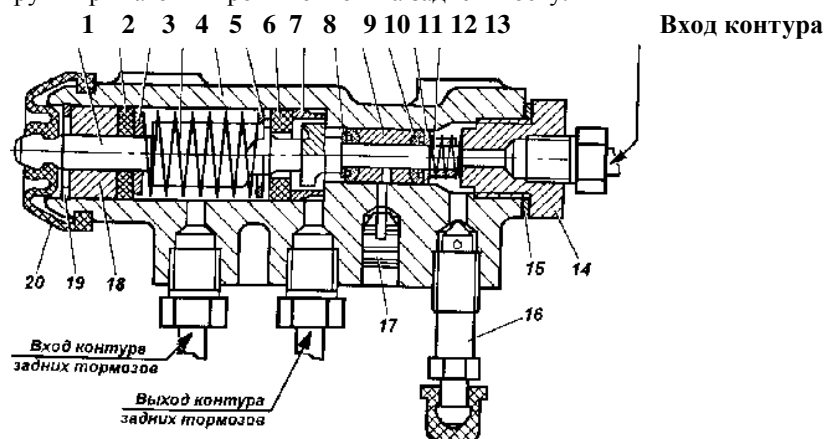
Регулятор давления: 1 -поршень; 2 -кольцо уплотнительное поршня; 3, 6 -шайба опорная пружины поршня; 4 – пружина поршня; 5 -корпус; 7 -уплотнитель головки поршня; 8-втулка корпуса; 9-шайба опорная втулки толкателя; 10-втулка толкателя; 11 –кольцо уплотнительное толкателя; 12 –тарелка опорная; 13 –пружина втулки толкателя; 14-пробка; 15-11прокладкапробки; 16-клапан перепускной; 17 -заглушка; 18 -втулка поршня; 19 -кольцо стопорное; 20 -чехол защитный
